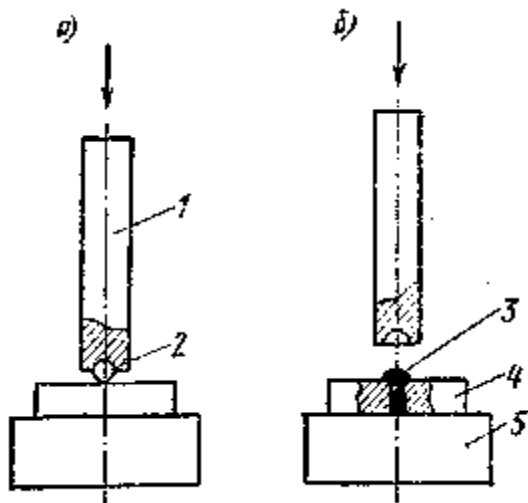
Приспособление для изготовления заклепок: а — изготовление обжимки; б — формовка головки заклепки
